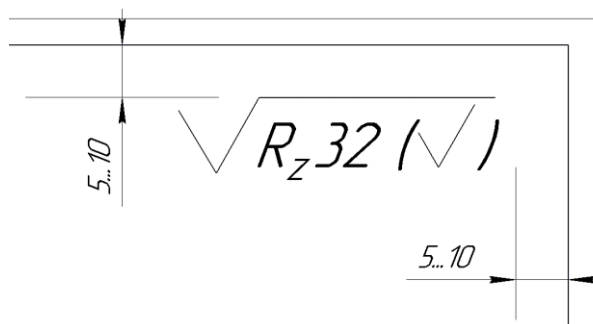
Обозначение одинаковой шероховатости для части поверхностей деталей
